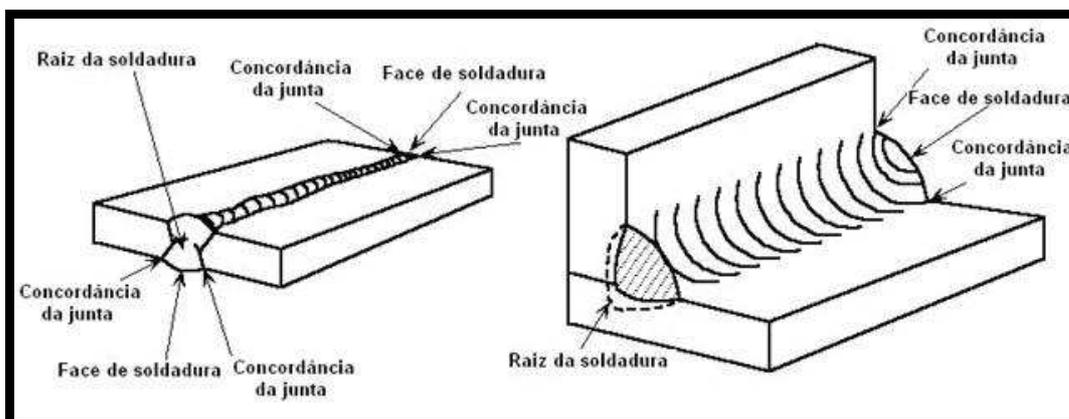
Exemplo de uma soldadura de topo a topo e uma soldadura de ângulo
